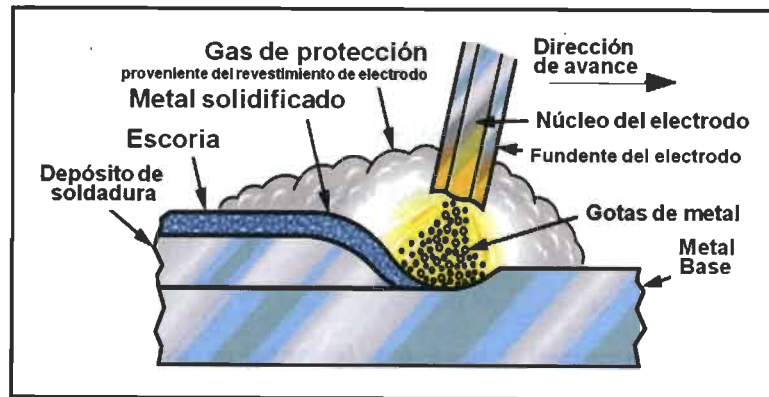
Diagrama Esquemático del Proceso de Soldadura SMAW (2).
